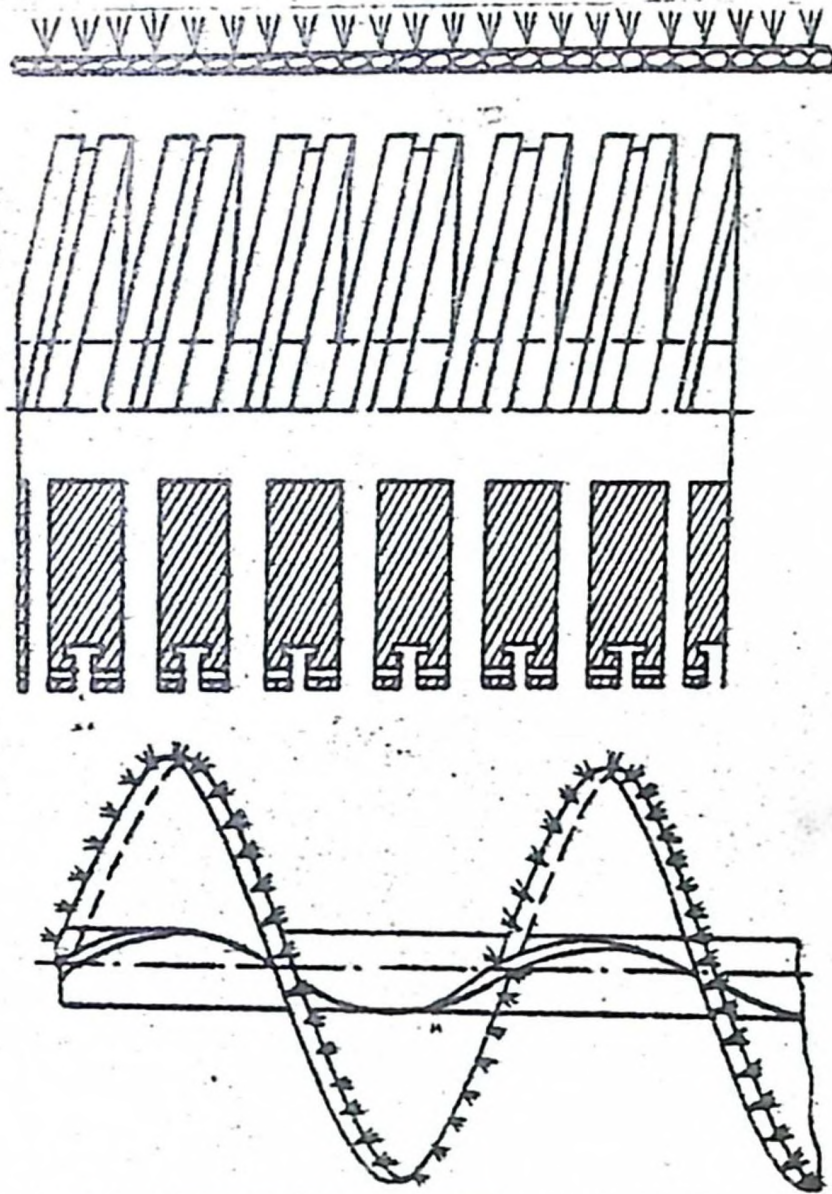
Изготовление полиэтиленового винта шнека со щеточным обрамлением
